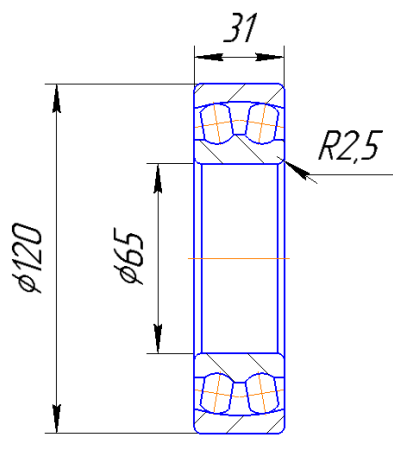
Эскиз подшипника 3513 ГОСТ 5721-75
